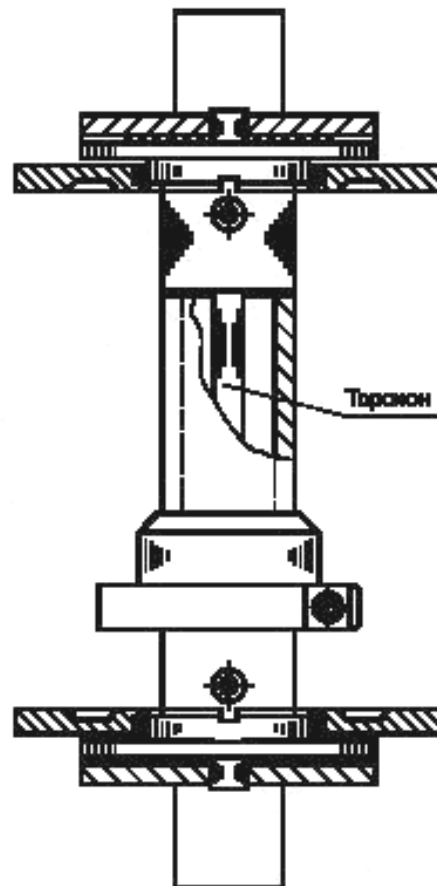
Типовое калибровочное устройство для безроторного сдвигового реометра (торсион)
